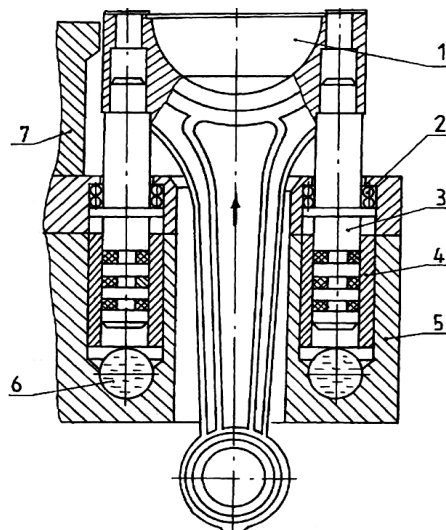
Пристосування з гідрозатискувачем для фрезерування площин роз'єму шатунів і кришок: 1 – сектор, 2 – пружина, 3 – плунжер, 4 – втулка, 5 – корпус, 6 – робоча рідина, 7 – направляюча.
